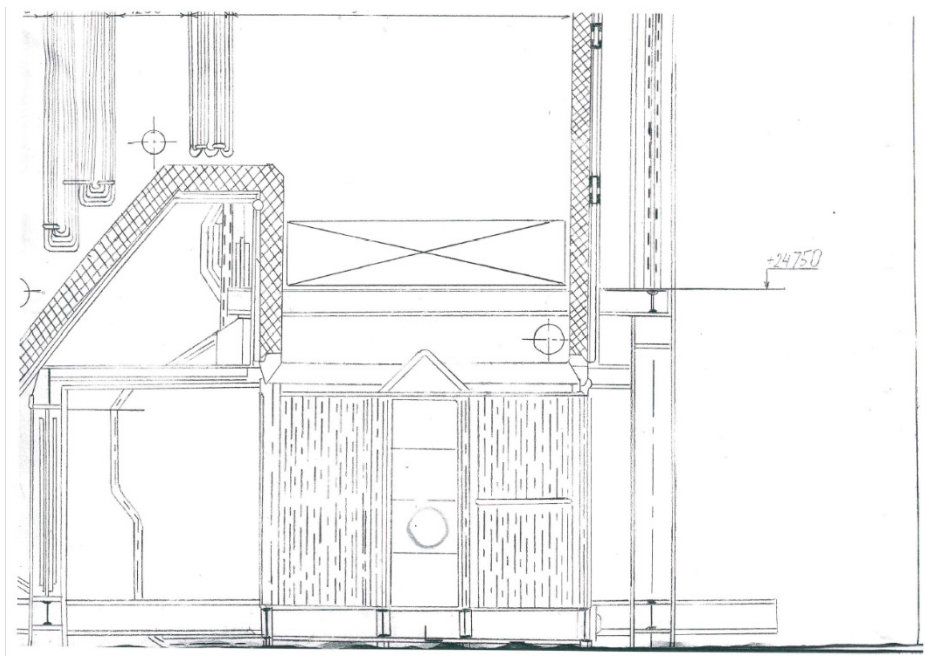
Сечение котла с трубчатым воздухоподогревателем [3]
